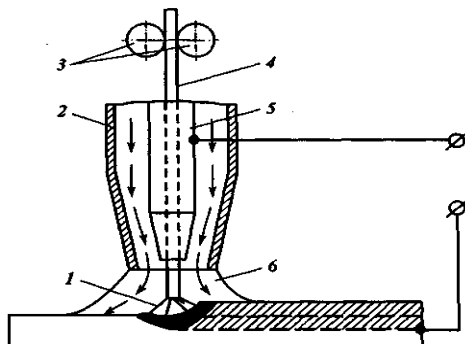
Схема сварки в среде CO_2 : 1 – сварочная дуга; 2 – сопло; 3 – роликовый механизм подачи проволоки; 4 – сварочная проволока (электрод); 5 – мундштук; 6 – зона защиты сварочной дуги углекислым газом
